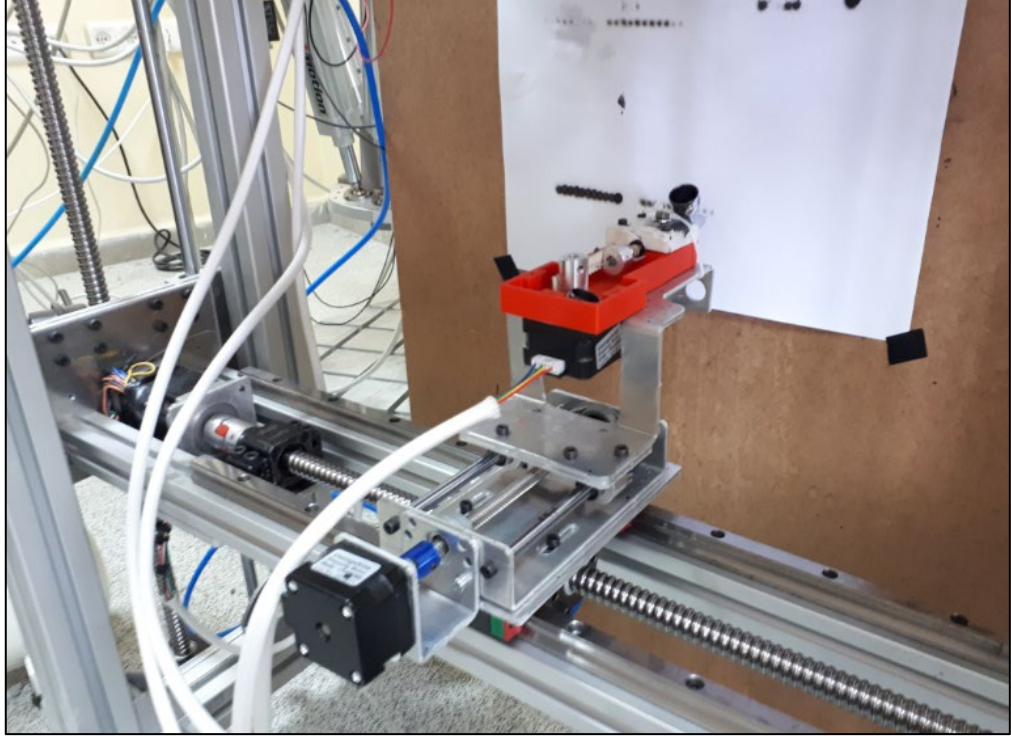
Taşıyıcı gövde montaj görüntüsü.
